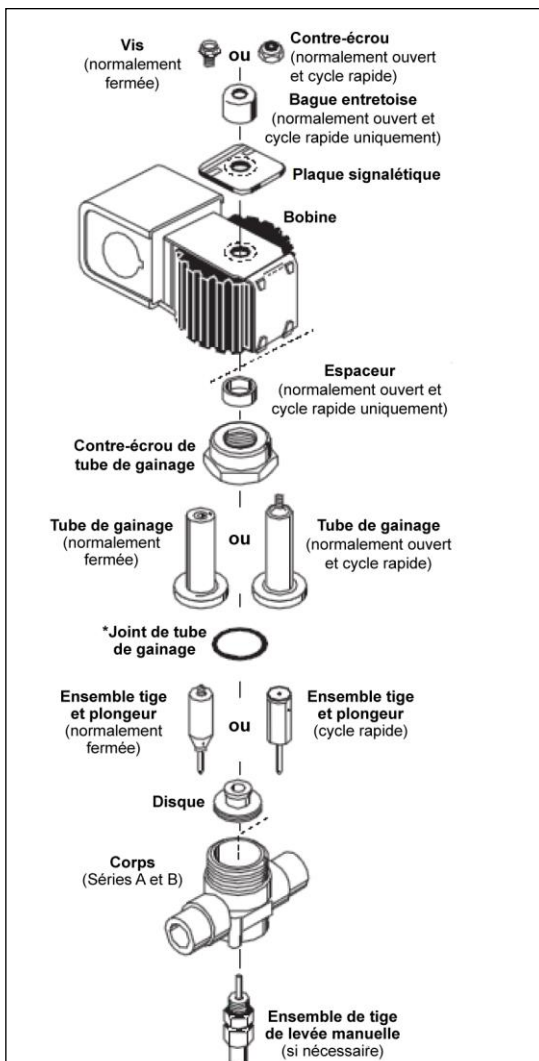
ÉLECTROVANNE CLASSIQUE DU RÉFRIGÉRANT 22044
